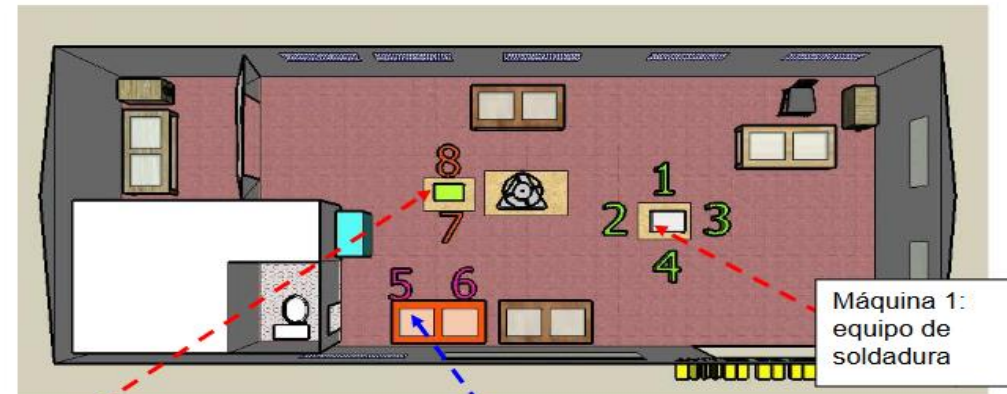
Puntos de medición, taller de Soldadura,
